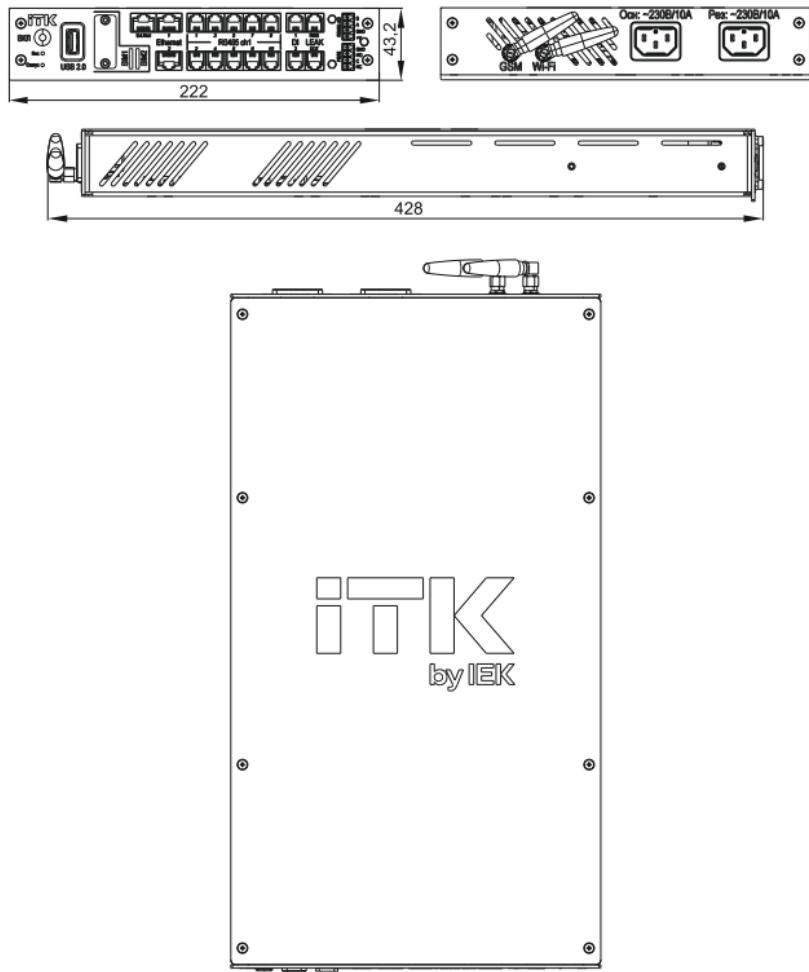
Внешний вид и габаритные размеры модуля / Figure 1 – Appearance and overall dimensions of the module / 1-сурет – Модульдің сыртқы түрі мен габариттік өлшемдері
